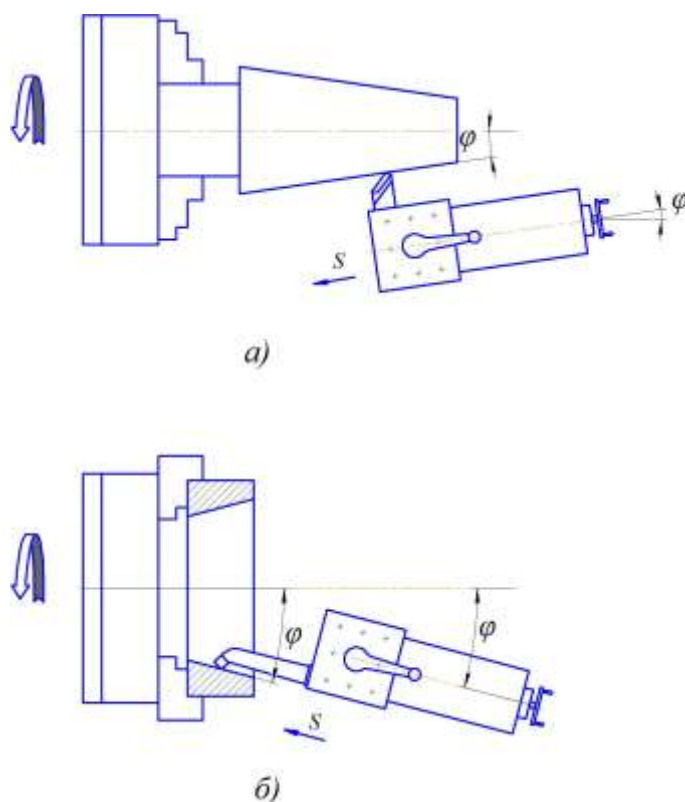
Обработка конических поверхностей при развернутой резцовой каретке суппорта: а) обтачивание наружной поверхности; б) растачивание внутренней поверхности
